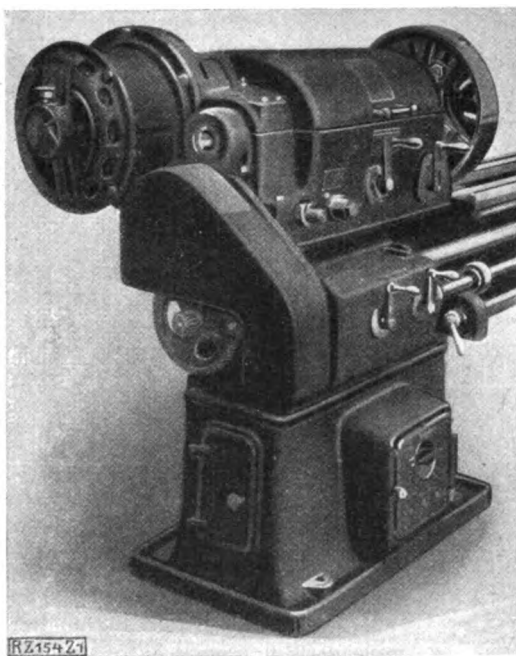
Spindelkasten mit Flanschmotor der Drehbank von Gebr. Böhlinger, G. m. b. H., Göppingen.
